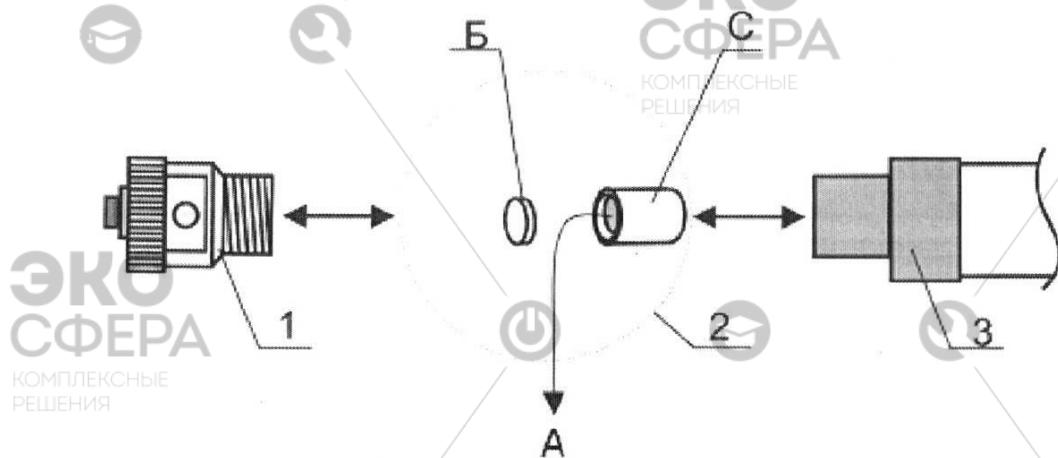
Схема извлечения деталей при замене наполнителя защитного патрона:
